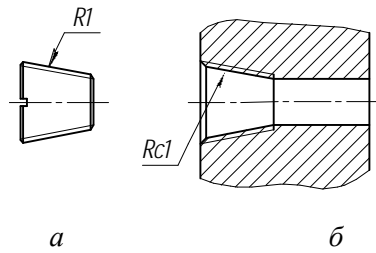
Нанесение размеров трубной конической резьбы:
